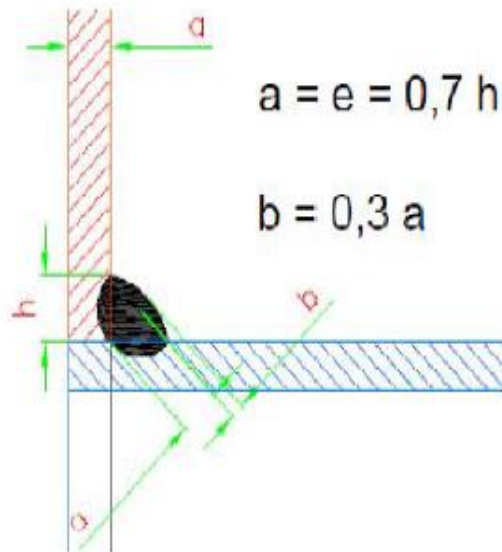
Boru ve flaş bağlantısının montaj resmi ve gerekli boyutsal ölçüleri
